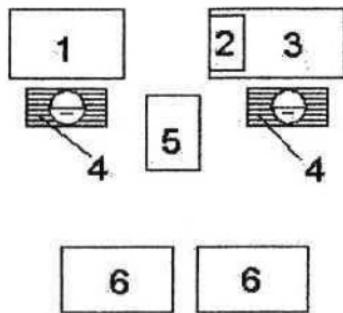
Примерная схема рабочего места сборщика: 1 – верстак слесарный; 2 – плита поверочная; 3 – стол сборщика; 4 – подставка под ноги; 5 – стол приемный передвижной; 6 – стеллаж-подставка
